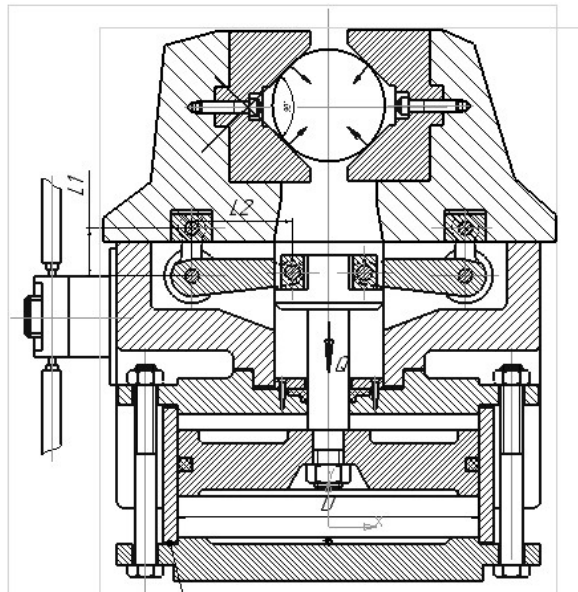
Загальний вигляд приводу пристрою
